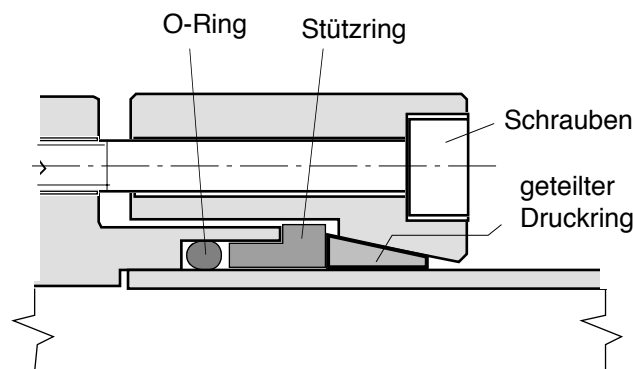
Kompakte Rohrverschraubungen mit O-Ring auf dem Umfang des angeschlossenen Rohrs
